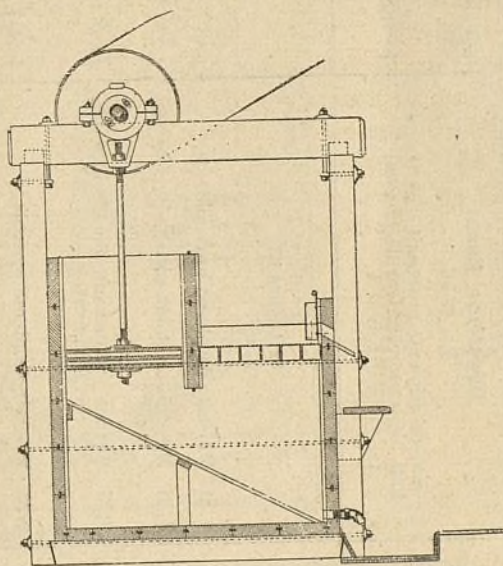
Coupe d'un jig mû par un excentrique avec le dispositif de M. Cooley.
